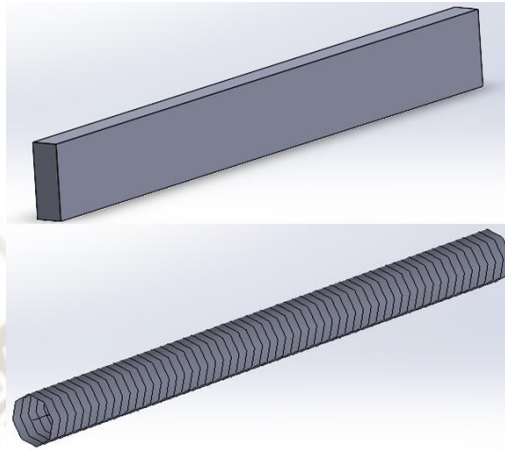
Interpretación cilíndrica de piezas geométricas
